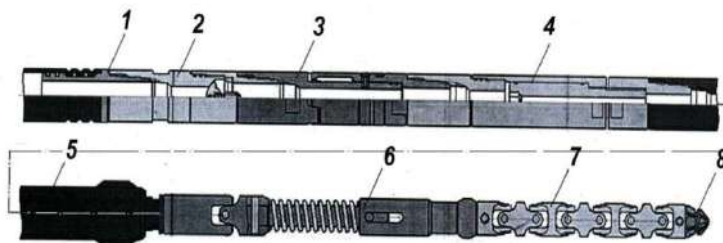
Комплект фрезеруючого обладнання для РРП
